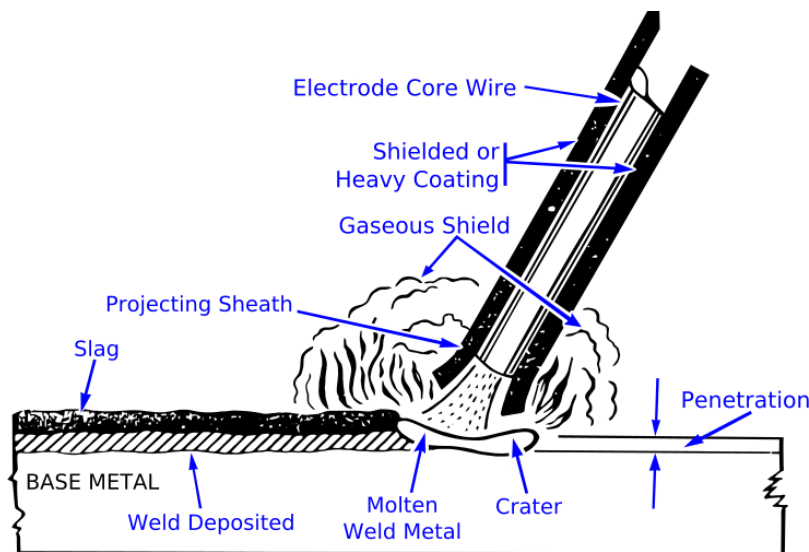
Schémas du procédé de soudage FCAW [87].
